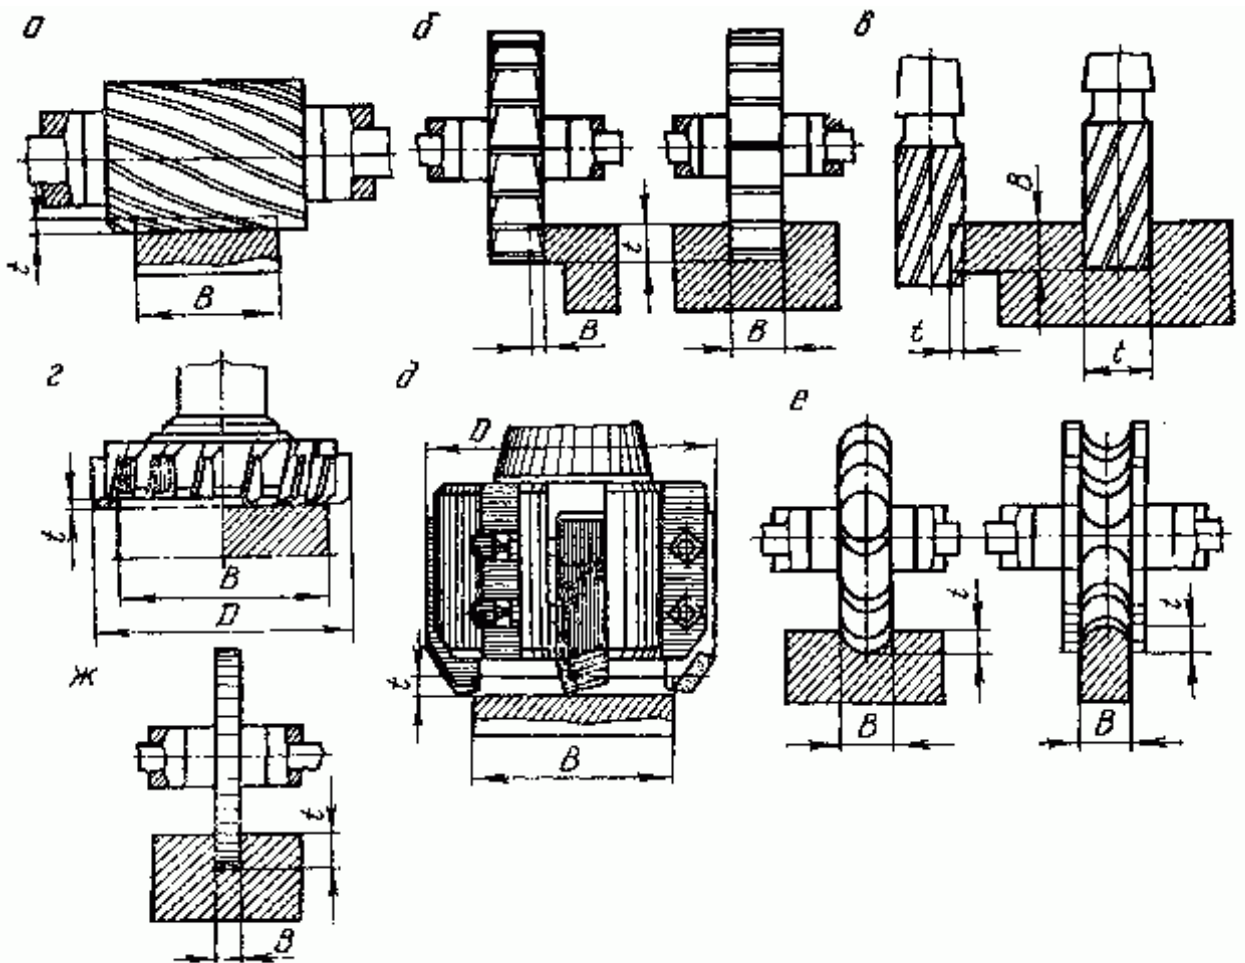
Типи фрез: а – циліндрична; б – дискова та пазова; в – кілцева; г, д – торцева; е – фасонна; ж – прорізна
